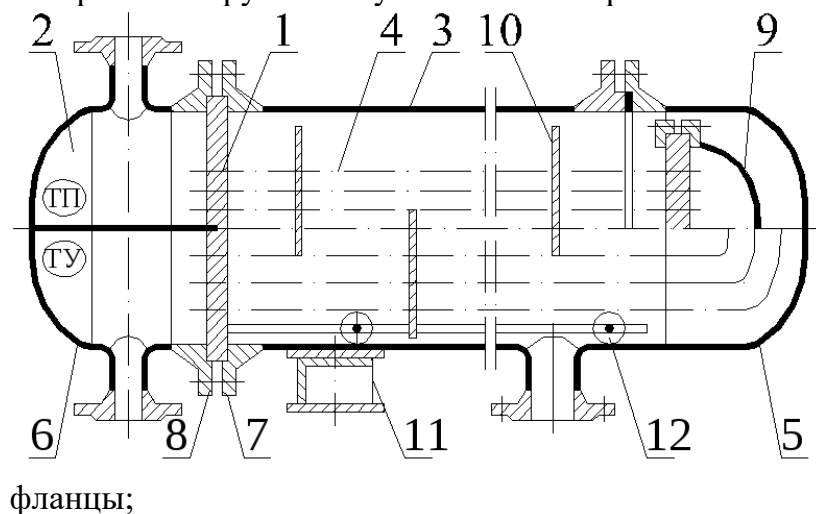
Двухходовой горизонтальный кожухотрубный теплообменник:
